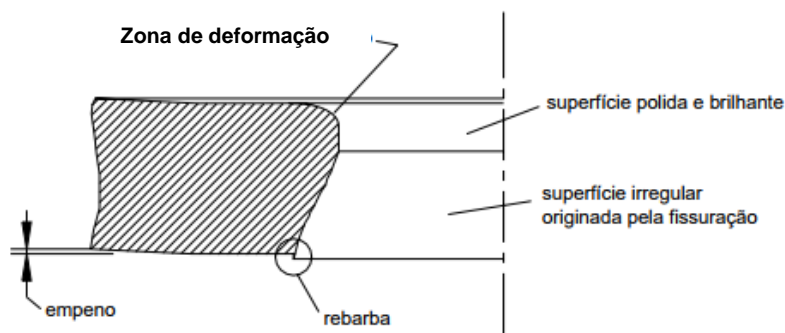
Composição de uma superfície de corte (retirada de [11])
